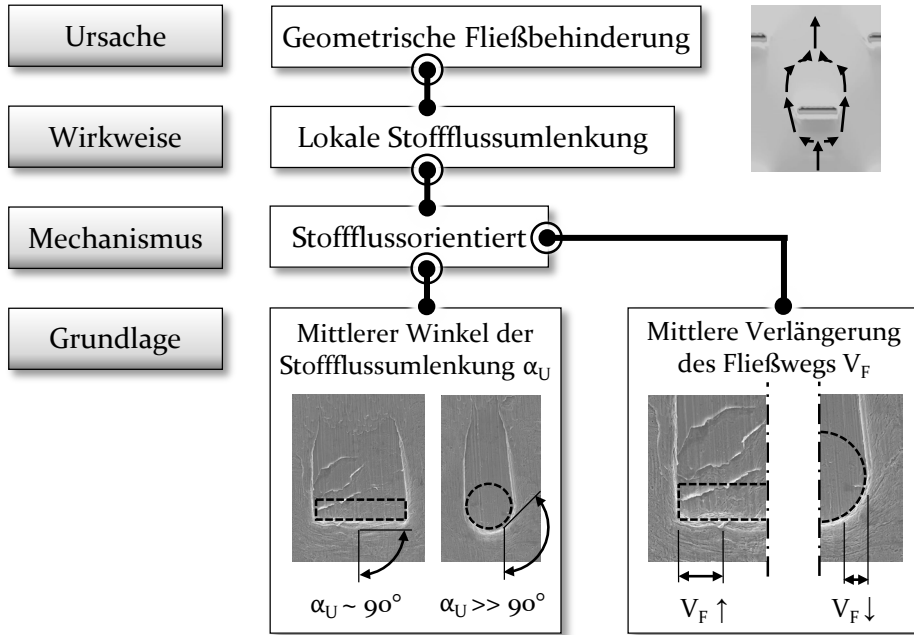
Wirkmechanismen erhabener Mikrotexturen auf Umformwerkzeugen
